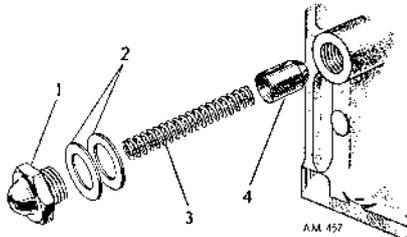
Das Öl-Überdruckventil befindet sich auf der rechten Seite hinten seitlich am Motorblock und besteht aus: 1 Mutter, 2 Fiberscheiben, 3 Druckfeder (sie darf nicht kürzer als 7,3 cm sein), 4 Überdruckventil
